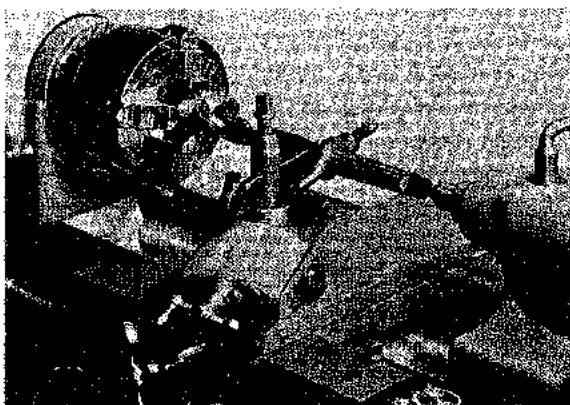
Disposición para taladrar grandes agujeros (Sheldon Machine Co., Inc.)
